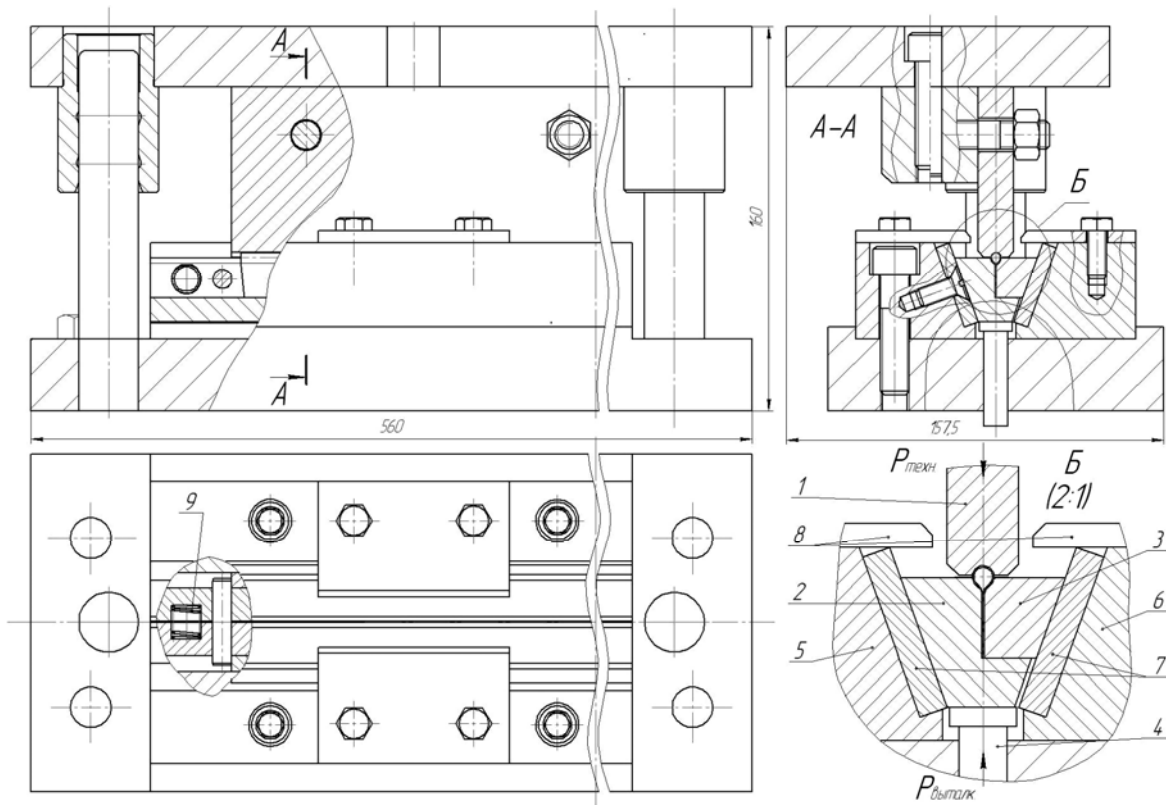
Штамп второго перехода штамповки детали «шторка» гибкой со сжатием:
